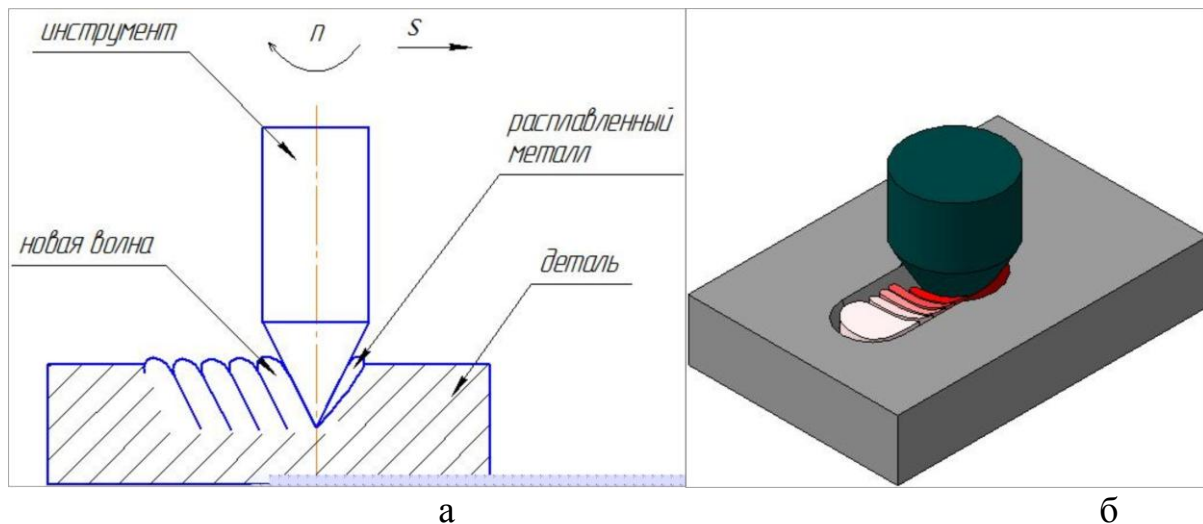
Локальное формирование рельефа поверхности легкоплавного металла коническим твердосплавным инструментом на основе практических навыков применения пластического сверления
